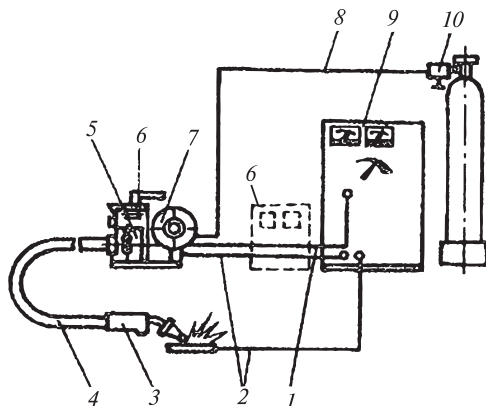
Монтажная схема установки для полуавтоматической сварки плавящимся электродом в среде защитного газа:
